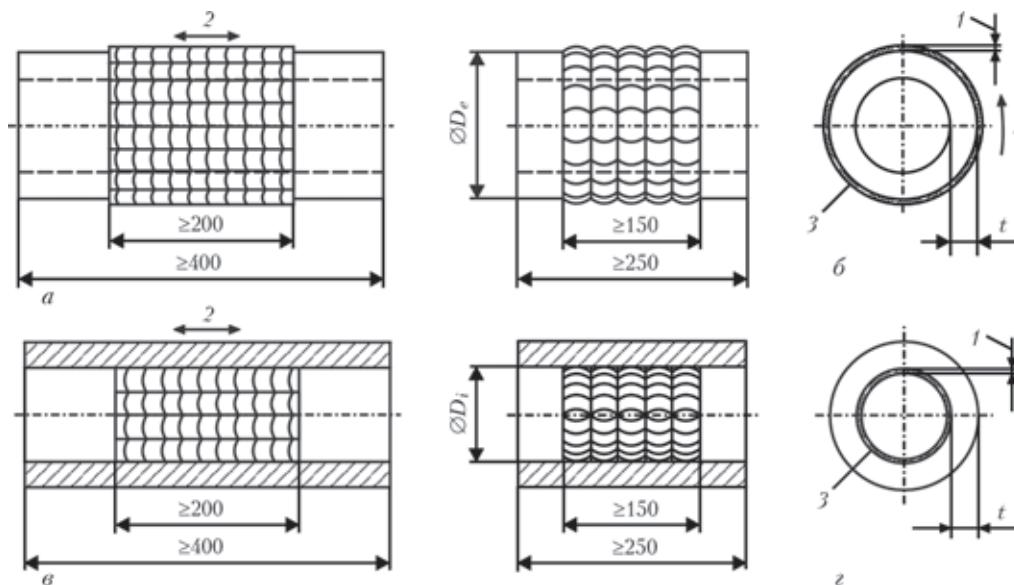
Наплавленный контрольный образец (труба): а — продольная наплавка наружной поверхности; б — кольцевая наплавка наружной поверхности; в — продольная наплавка внутренней поверхности; г — кольцевая наплавка внутренней поверхности (1 — буферный слой (подслой, наплавляется по необходимости); 2 — направление наплавки; 3 — номера слоев согласно рWPS или общая толщина наплавленного слоя; D_e — наружный диаметр трубы; D_i — внутренний диаметр трубы; t — толщина основного металла) [1]
